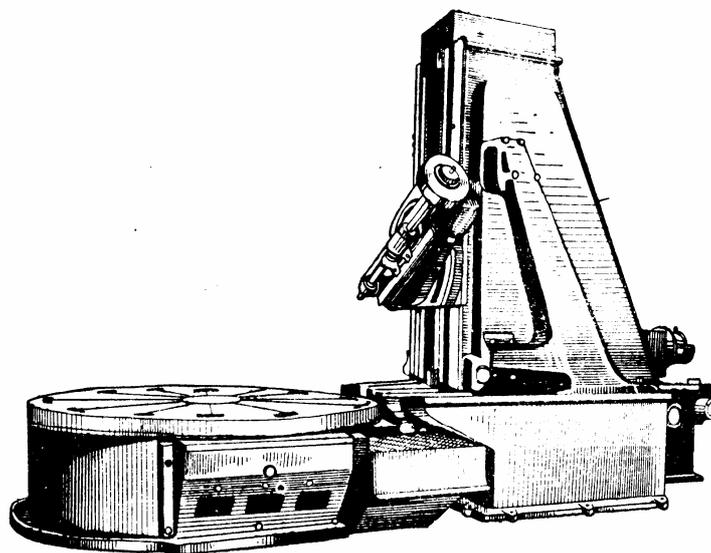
Вертикальный зубофрезерный станок с подающей стойкой без поддерживающей колонны
